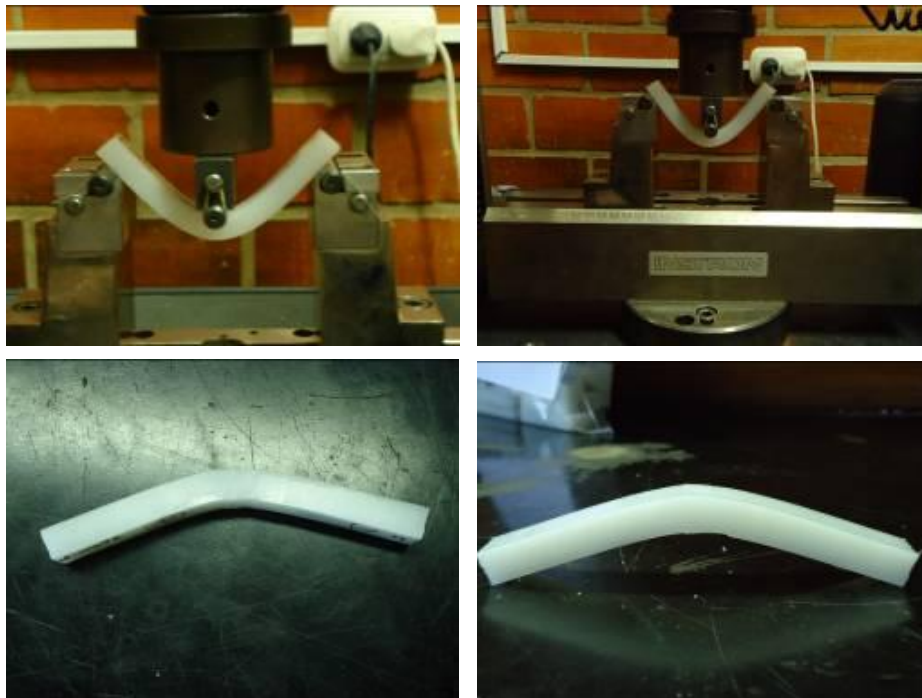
Ensayo de flexión en 3 puntos de una probeta soldada extraída del borde de la placa.
